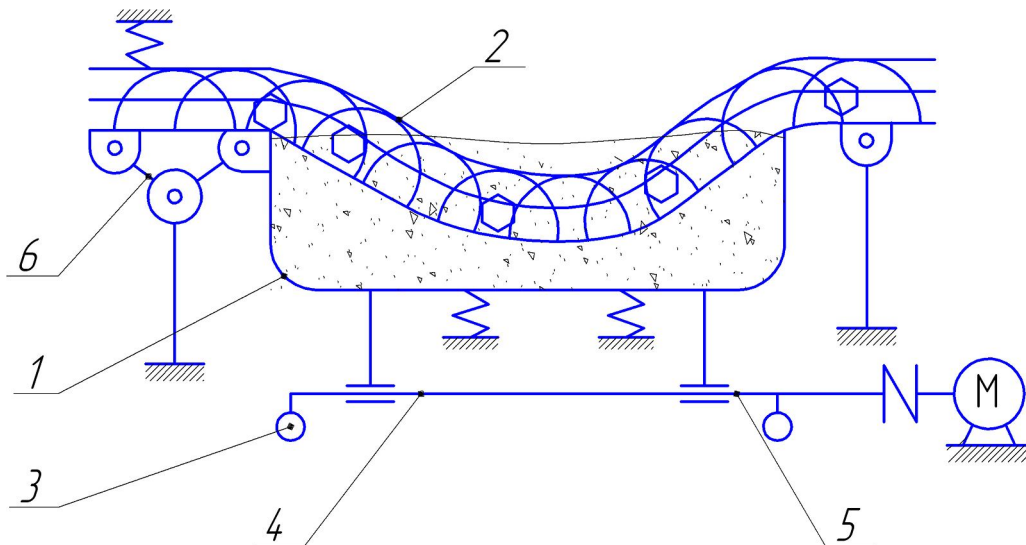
Принципова схема вібраційної машини безперервної дії з гнучкою робочою камерою: 1 – контейнер; 2 – труба з гнучкого матеріалу; 3 – дебаланс; 4 – приводний вал; 5 – робочий наповнювач; 6 – двоплечевий важіль
